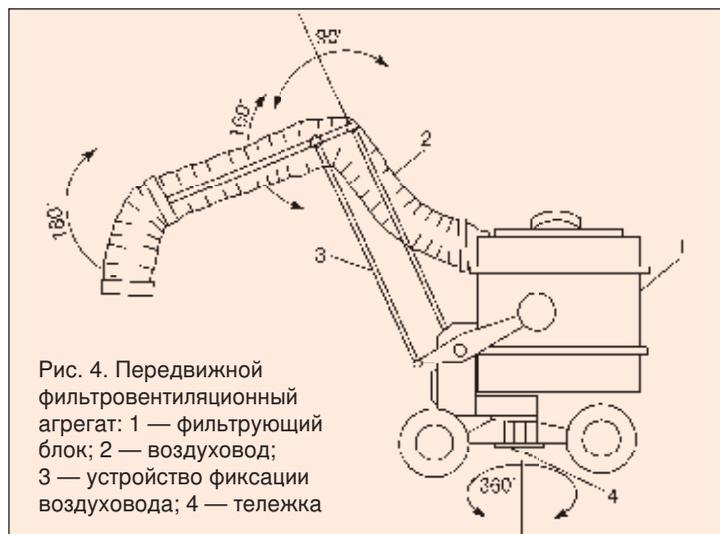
Передвижной фильтровентиляционный агрегат: 1 — фильтрующий блок; 2 — воздуховод; 3 — устройство фиксации воздуховода; 4 — тележка
